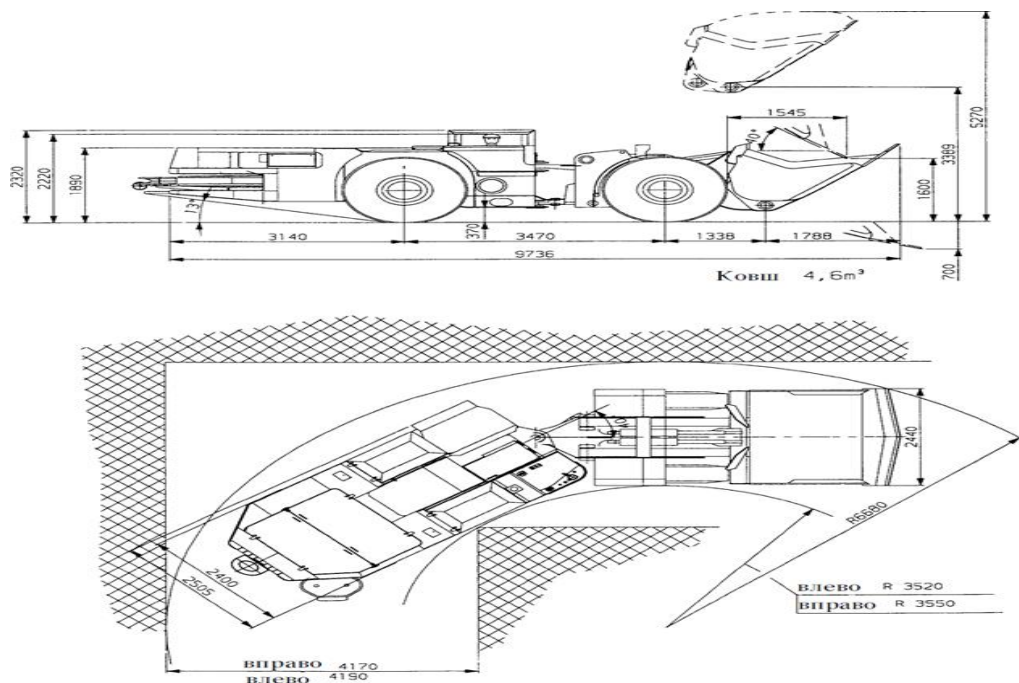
3 – Общий вид с габаритными размерами ПДМ Sandvik LH409E
